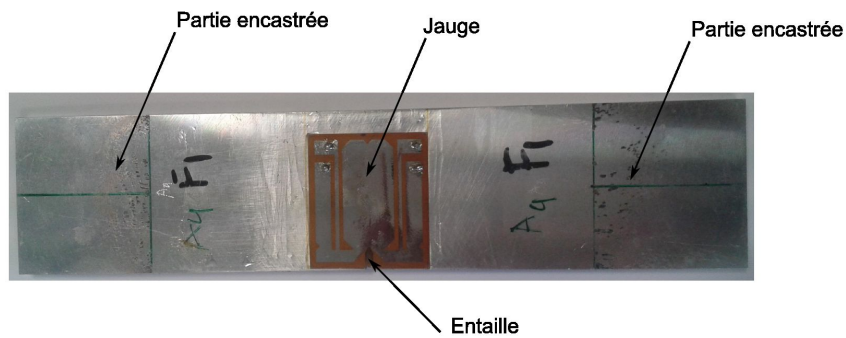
Montage de l'essai de fissuration
